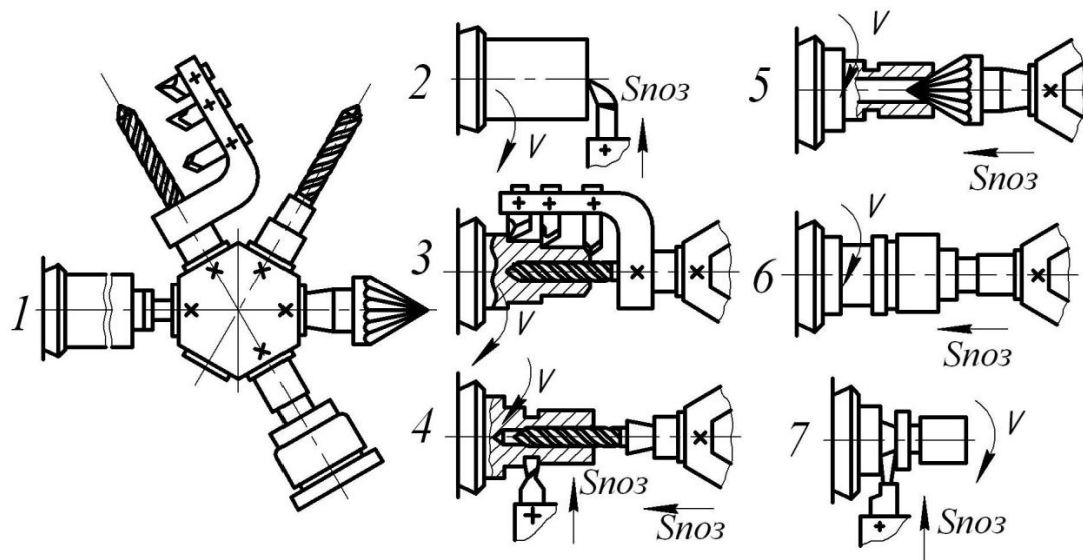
Схеми обробки поверхонь заготовки на токарно-револьверному верстаті: 1 – подача прутка до упору; 2 – підрізання правого торця; 3 – обточування двох циліндричних поверхонь, знімання фаски і свердління отвору; 4
